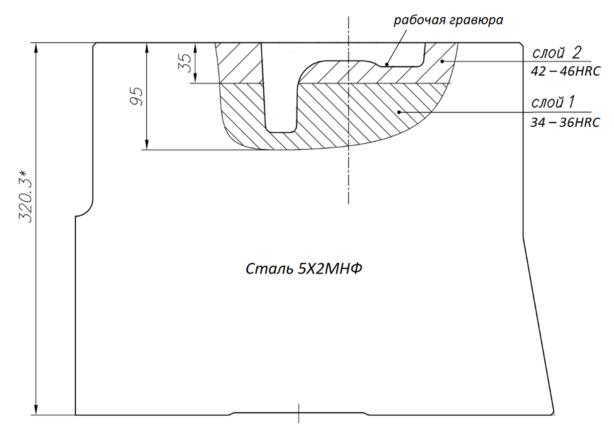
Схема расположения рабочей гравюры штампа в наплавленных слоях металла
